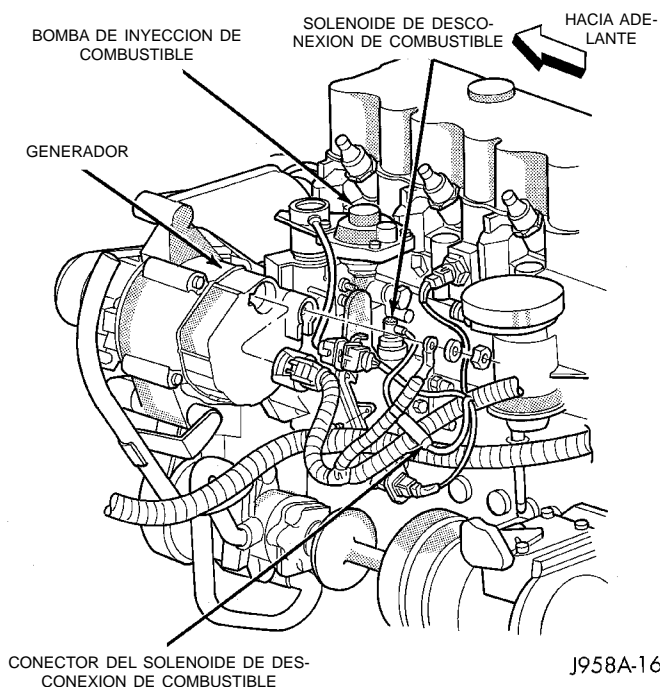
Conector del solenoide de desconexión de combustible - Motor diesel
